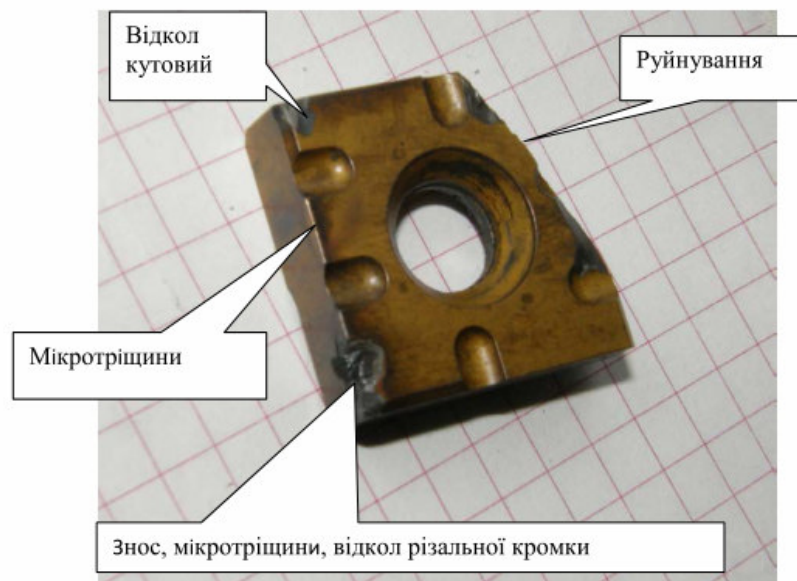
Види пошкодження та руйнування змінної фрезерної пластини SNGX250800CM30M
